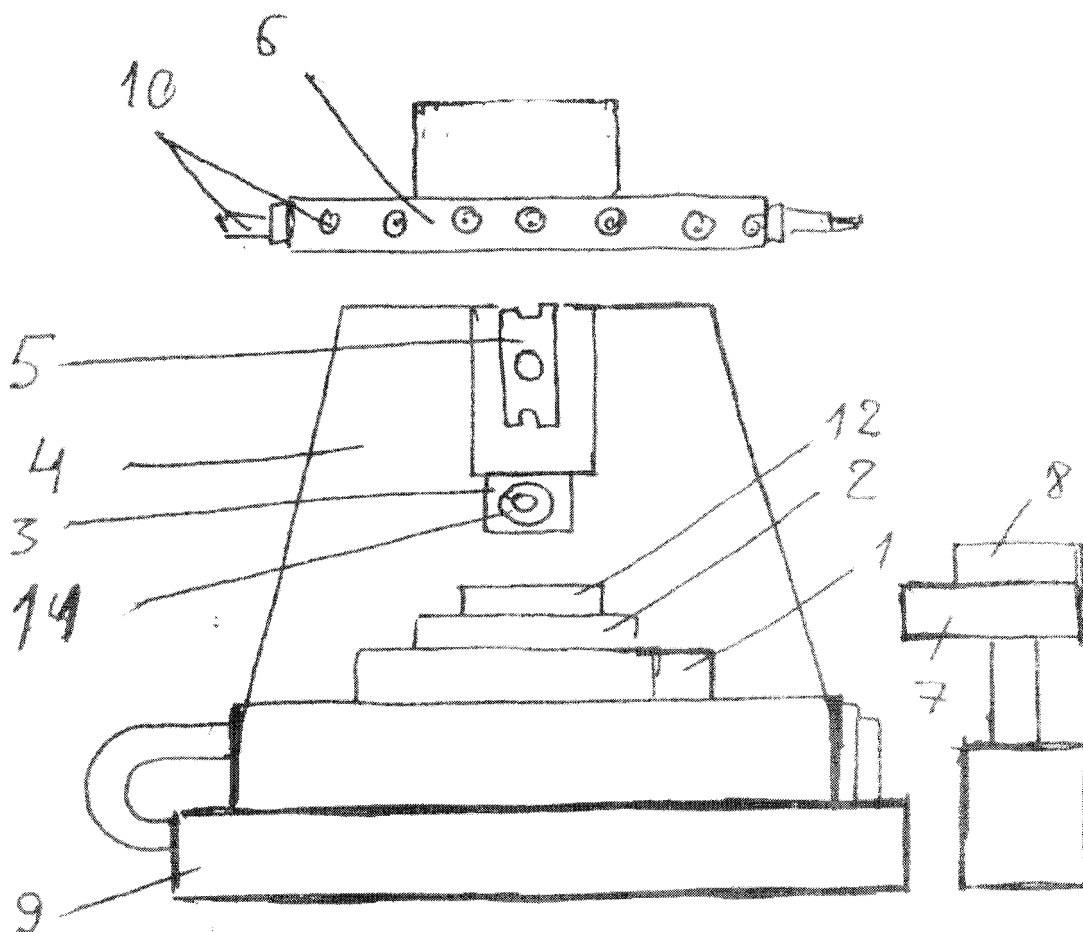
Общий вид многоцелевого станка модели ИР500ПМФ4
